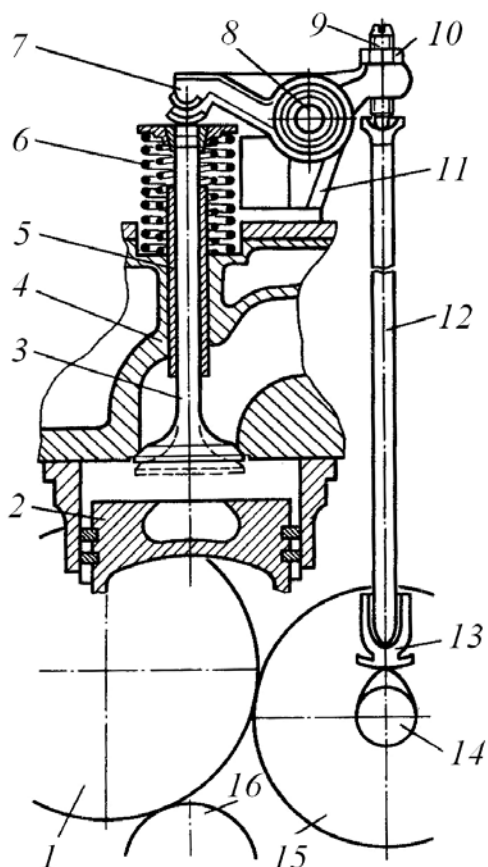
Схема распределительного механизма ОНВ с верхним расположением клапана и нижним распределительного вала:
